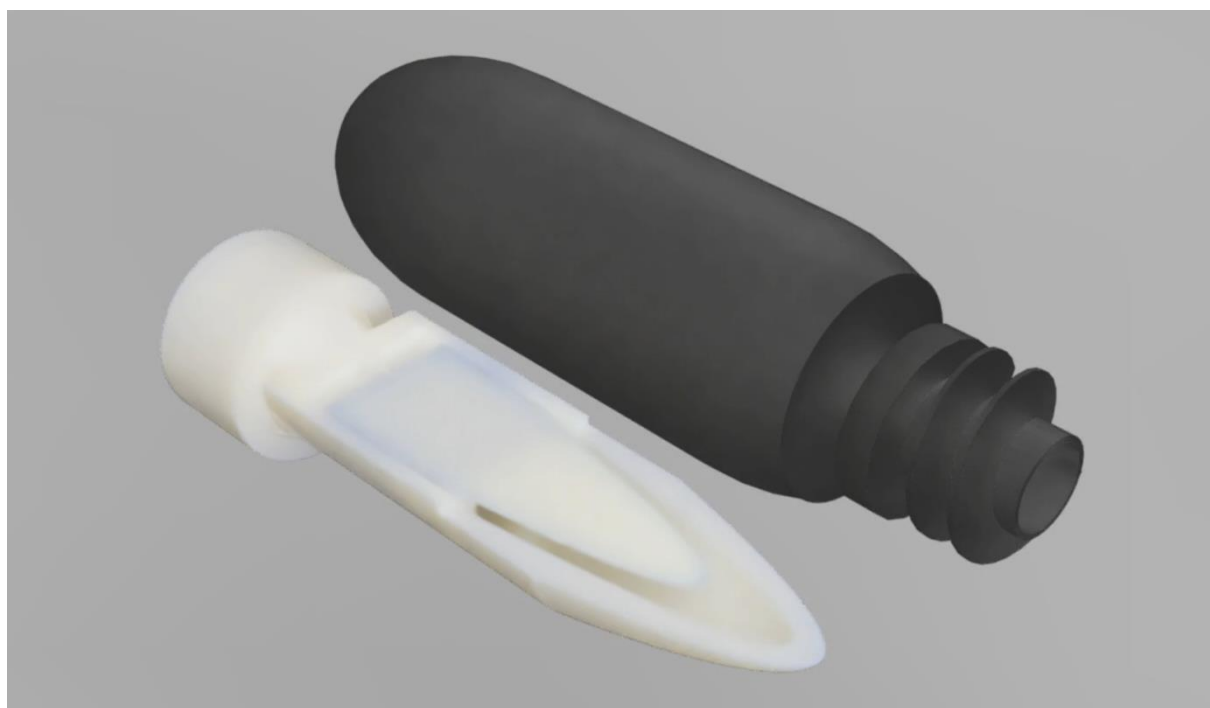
Трехмерное изображение устройства и резервуара для пищи
